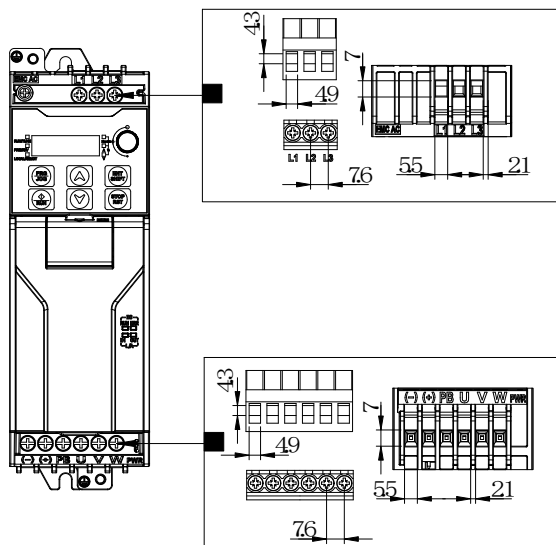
Клеммы главной цепи (Типоразмер типа В)
